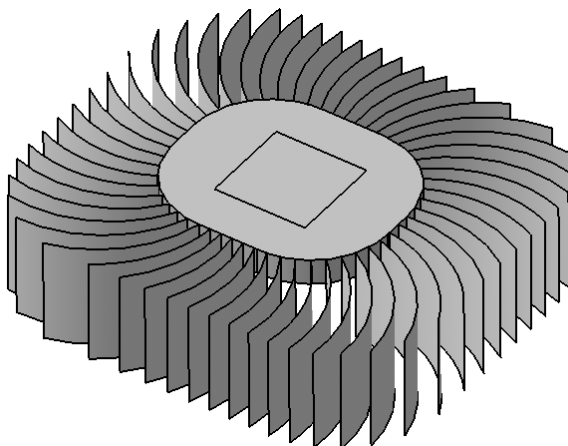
Modelo 3D em CAD do dissipador patente 6671172B2.
